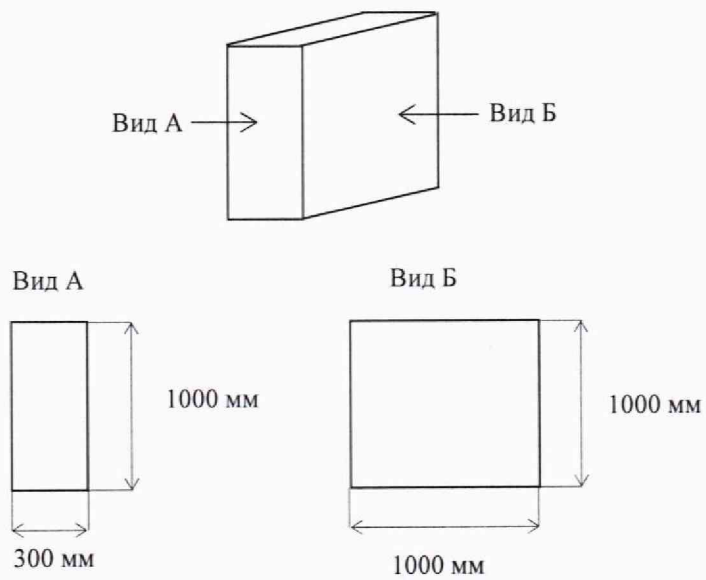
Внешний вид имитатора габаритных размеров № 4
